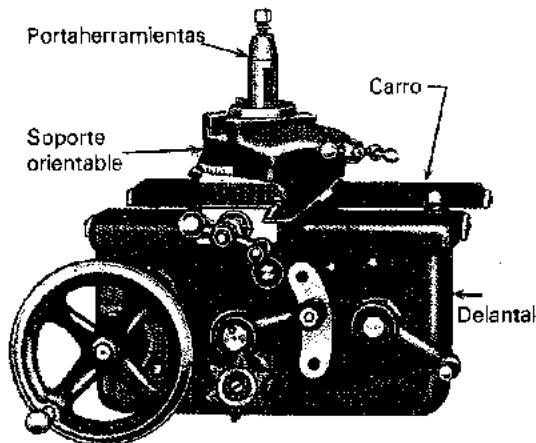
Carro principal del torno (South Bend Lathe Works).
